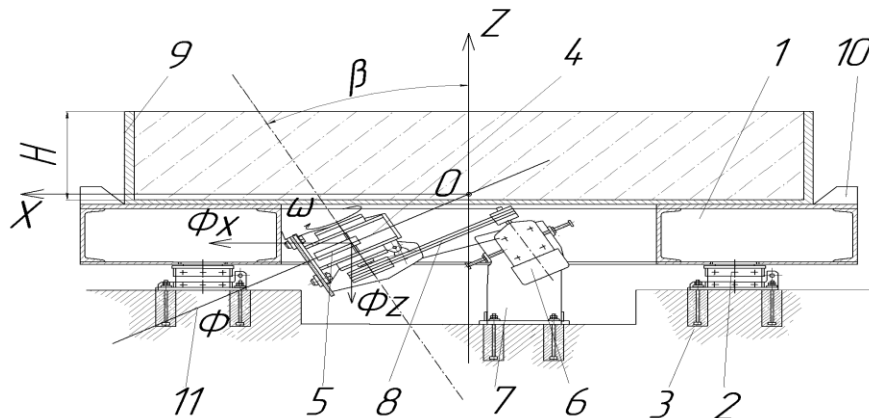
Розрахункова схема динамічної системи «віброплощадка – цементобетонне середовище»: 1 – рухома рама віброплощадки; 2 – пружна опора; 3 – фундамент; 4 – вібробуджувач; 5 – дебаланс; 6 – електродвигун; 7 – піддвигунева рама; 8 – клинопасова передача; 9 – форма із цементобетонною сумішшю; 10 – клиновий упор; 11 – площина обертання дебалансу.
